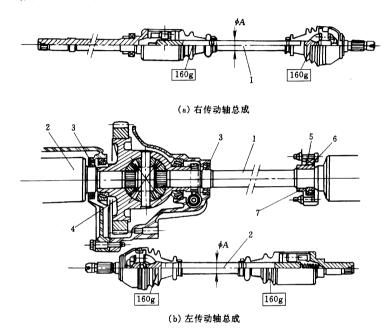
传动轴的安装 1. 右传动轴总成 2. 左传动轴总成 3. 差速器油封 4. 半轴齿轮 5. 螺栓 6. 轴承 7. 轴承衬套
